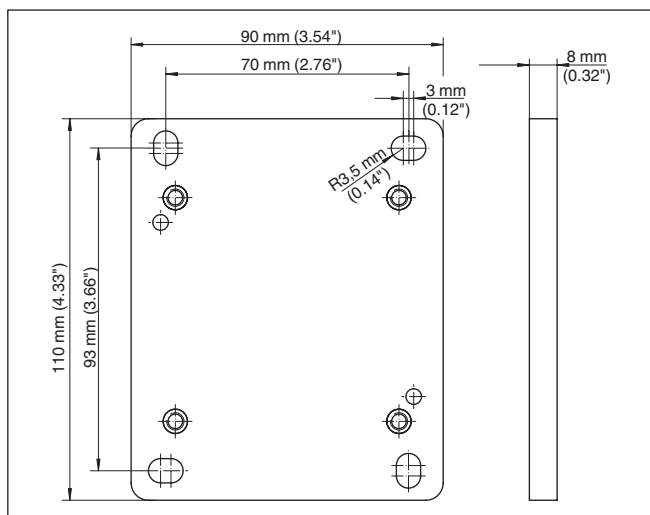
Gabarito dos orifícios - Placa de montagem na parede
